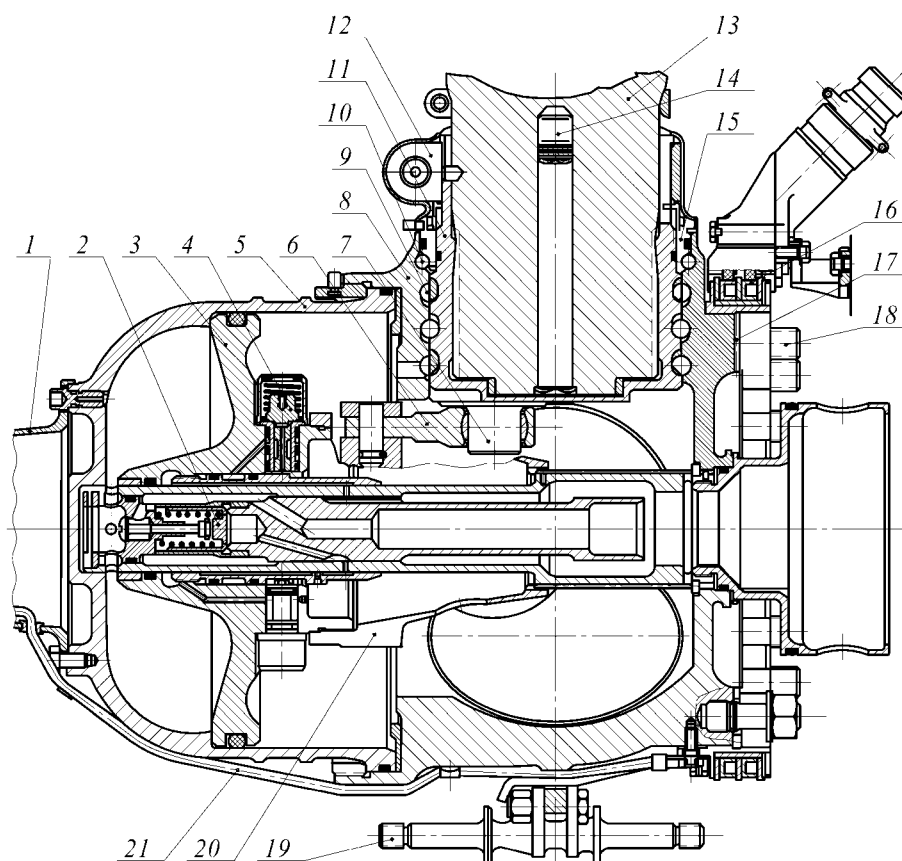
Конструктивная схема втулки винта АВ-68: 1- трубка для установки обтекателя, 2- клапан гидравлического фиксатора шага, 3- поршень, 4- клапан центробежного фиксатора шага винта, 5- цилиндр, 6- шатун, 7- палец стакана, 8- корпус втулки, 9- подшипник с сепаратором (заштриховано), 10- упорный подшипник, 11- стакан, в который вворачивается на резьбе лопасть, 12- хомут и штифт, фиксирующие лопасть в стакане, 13- лопасть, 14- балансировочный груз, 15- гайка стакана, 16- щётки токосъёмника обогрева лопастей и обтекателя, 17- торцевые шлицы на корпусе, 18- шпильки крепления винта к валу винта, 19- кронштейны крепления обтекателя, 20- траверса, 21- электропровод обогрева обтекателя
